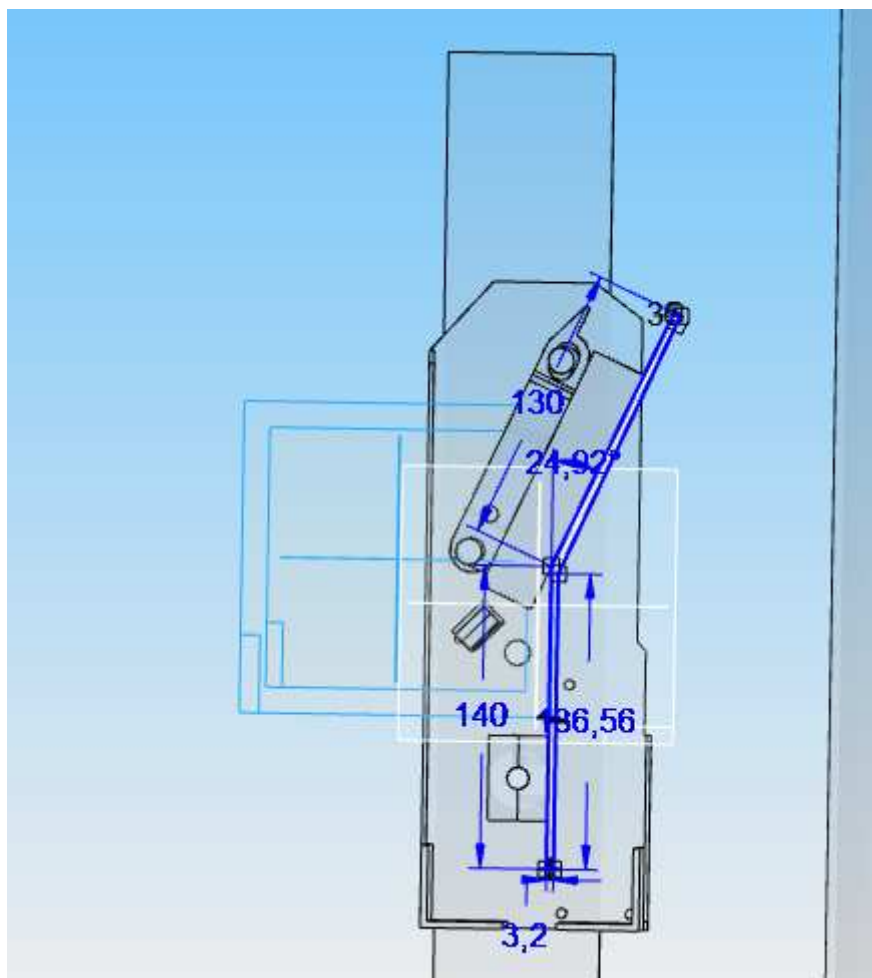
Croqui da vista superior do braço de fixação da haste do sensor, montado no conjunto elevatório.
